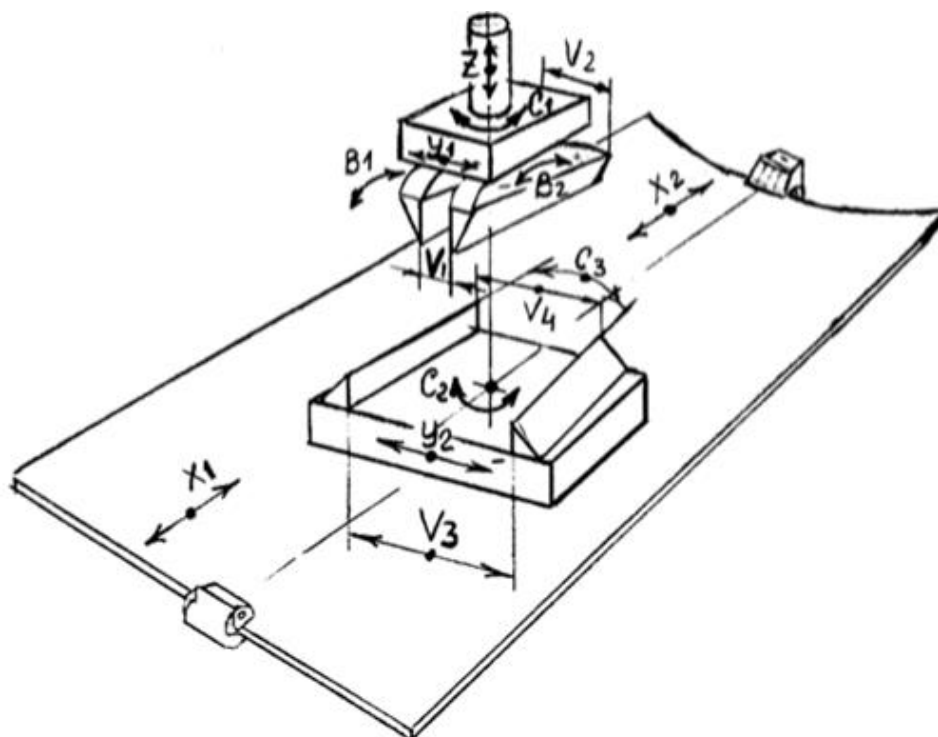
Схема рабочих и установочных перемещений прессы СПП-250
